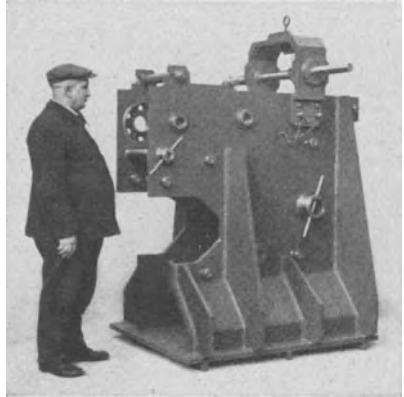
Geschweißte Bohrvorrichtung.
